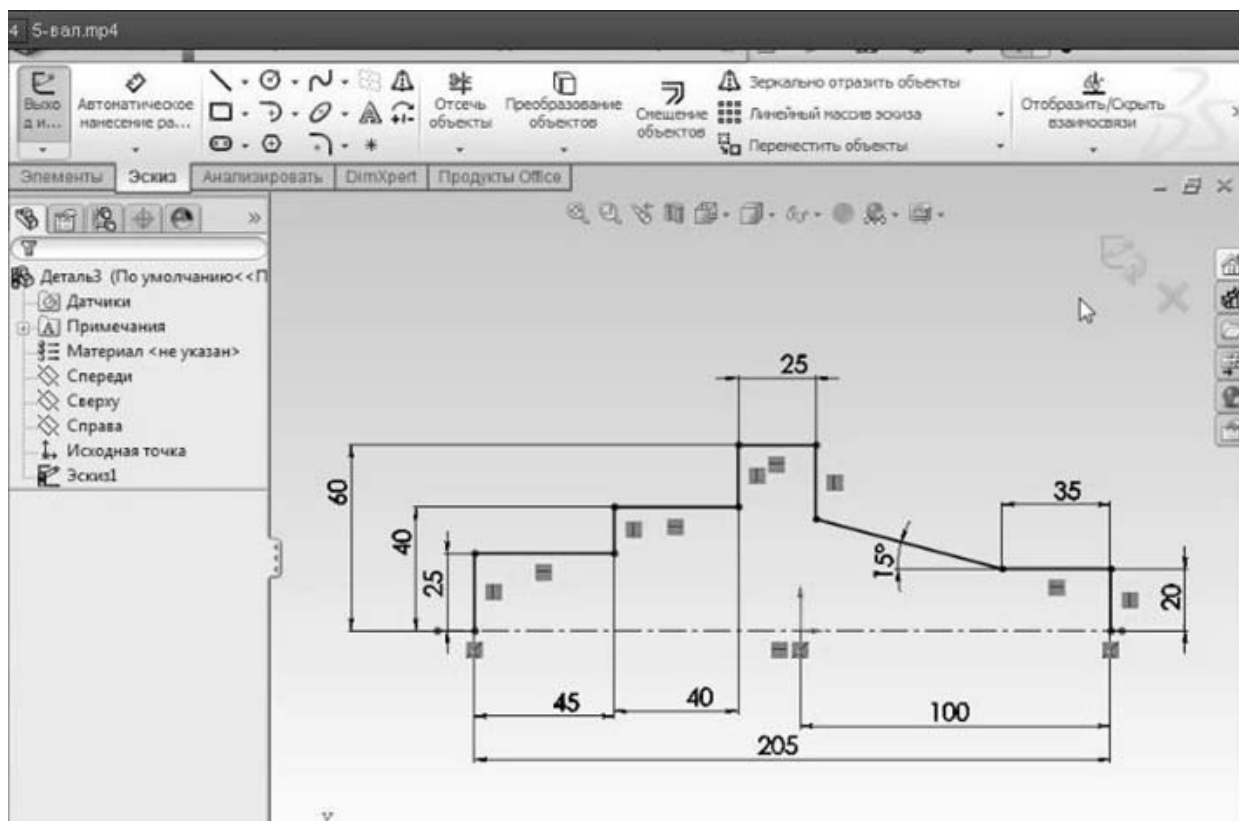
Пример эскиза вала с проставленными размерами
